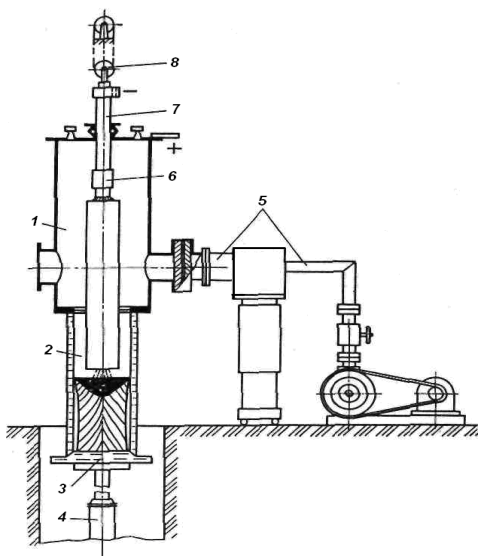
Схема конструкції вакуумної дугової печі
